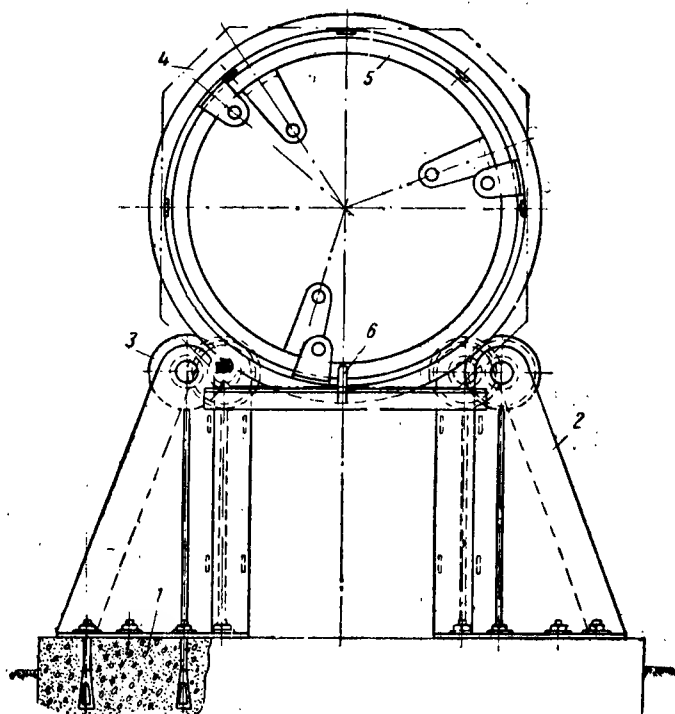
Стенд для сборки полюсов в остова тягового двигателя:
